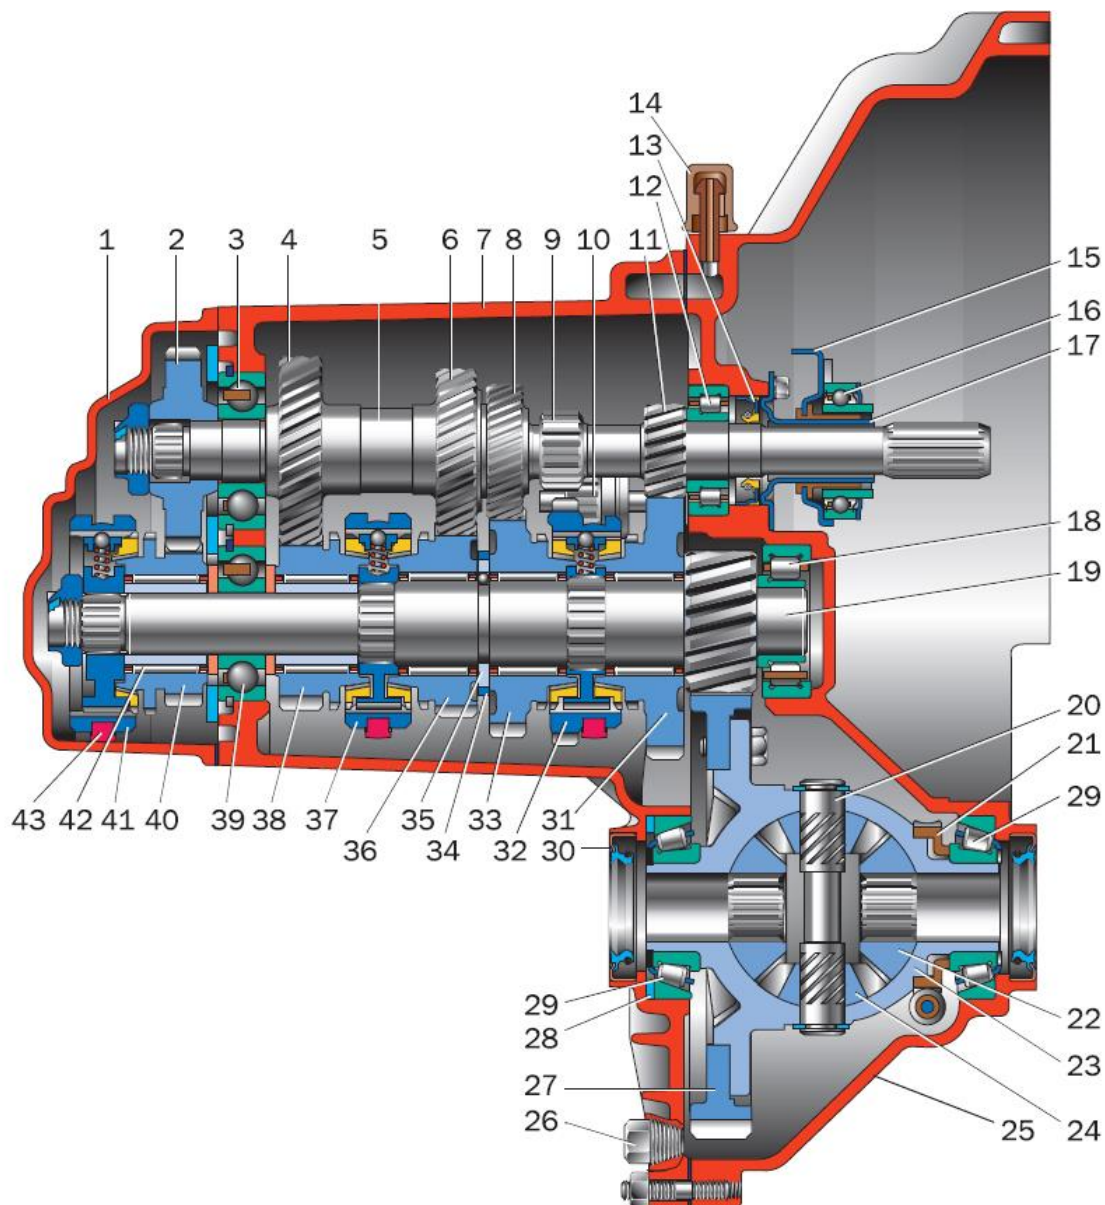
Пятиступенчатая двухвальная коробка передач легкового автомобиля с поперечным расположением двигателя: 1 – задняя крышка картера коробки передач; 2 – ведущая шестерня V передачи; 3 – шариковый подшипник первичного вала; 4 – ведущая шестерня IV передачи первичного вала; 5 – первичный вал; 6 – ведущая шестерня III передачи первичного вала; 7 – картер коробки передач; 8 – ведущая шестерня II передачи первичного вала; 9 – шестерня заднего хода; 10 – промежуточная шестерня заднего хода; 11 – ведущая шестерня I передачи первичного вала; 12 – роликовый подшипник первичного вала; 13 – сальник первичного вала; 14 – сапун; 15 – фланец муфты; 16 – подшипник выключения сцепления; 17 – направляющая втулка муфты; 18 – роликовый подшипник вторичного вала; 19 – вторичный вал; 20 – ось сателлитов; 21 – ведущая шестерня привода спидометра; 22 – шестерня полуоси; 23 – коробка дифференциала; 24 – сателлит; 25 – картер сцепления; 26 – пробка для слива масла; 27 – ведомая шестерня главной передачи; 28 – регулировочное кольцо; 29 – роликовый конический подшипник дифференциала; 30 – сальник полуоси; 31 – ведомая шестерня I передачи вторичного вала; 32 – синхронизатор I и II передач; 33 – ведомая шестерня II передачи вторичного вала; 34 – стопорное кольцо; 35 – упорное полукольцо; 36 – ведомая шестерня III передачи вторичного вала; 37 – синхронизатор III и IV передач; 38 – ведомая шестерня IV передачи вторичного вала; 39 – шариковый подшипник вторичного вала; 40 – ведомая шестерня V передачи вторичного вала; 41 – синхронизатор V передачи; 42 – игольчатый подшипник; 43 – вилка переключения передач
